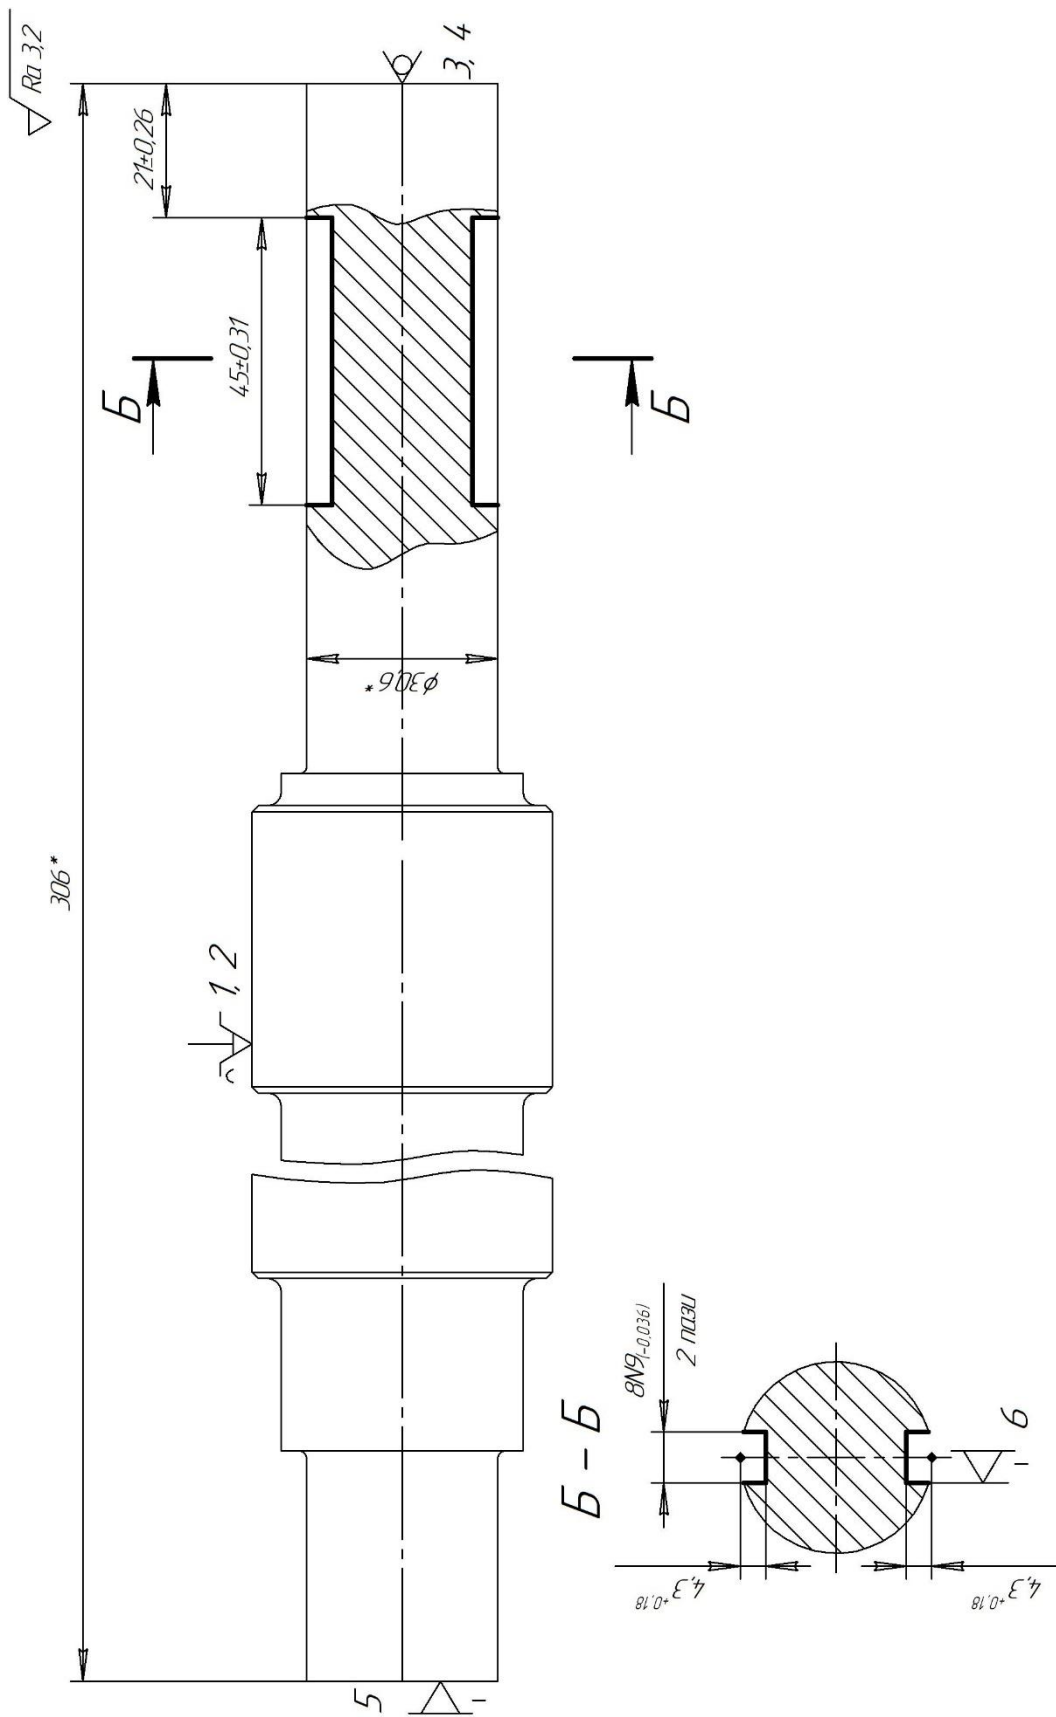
Альтернативна схема базування заготовки на операції 040 фрезерній з ЧПК
